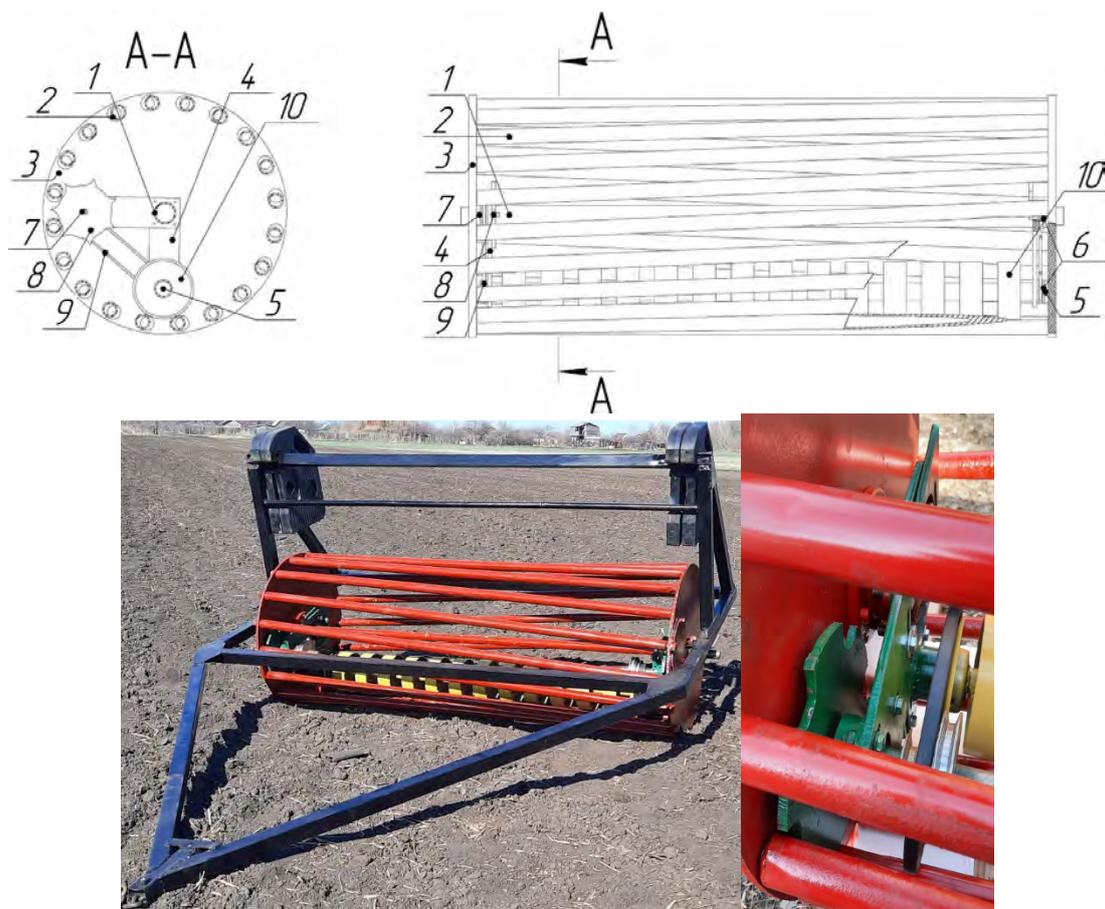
Пруtkово-дисковый каток: 1 – ось пустотелого цилиндра; 2 – прутки; 3 - вертикальные диски; 4 - Г-образные крепления; 5 - дополнительная ось; 6 – шкивы; 7 - вспомогательные оси; 8 – звездочки; 9 - ременная передача; 10 - вспомогательные диски
